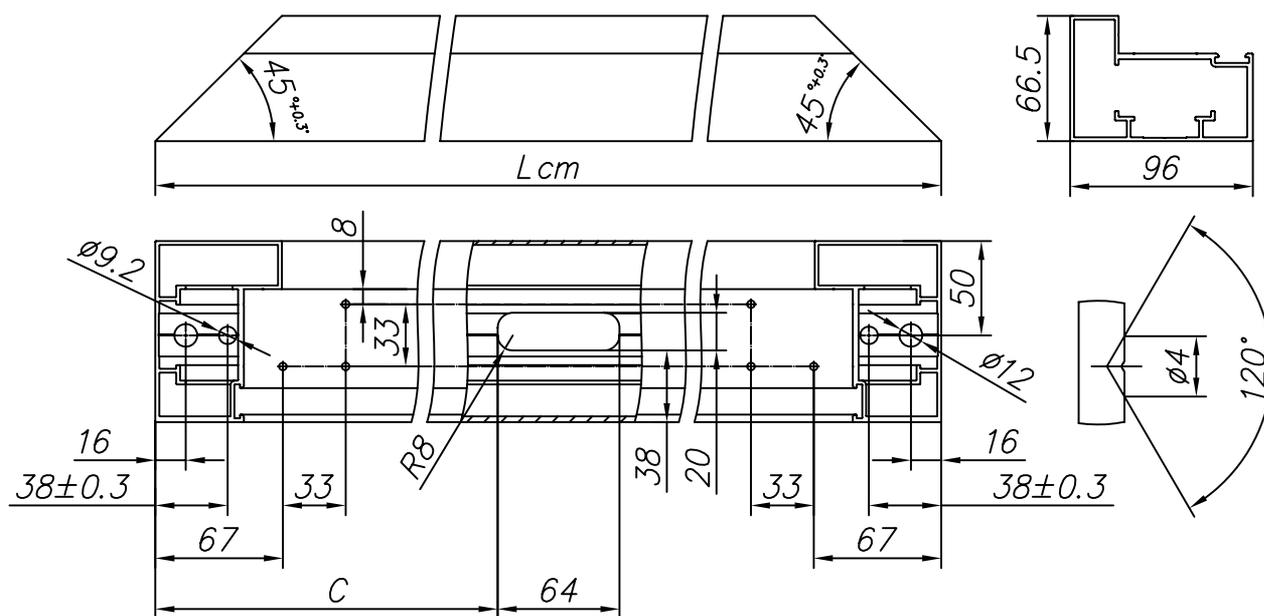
Изготовление стойки FLGU.400.0102 с пазом под ответную планку замка FLGU.400.1012
